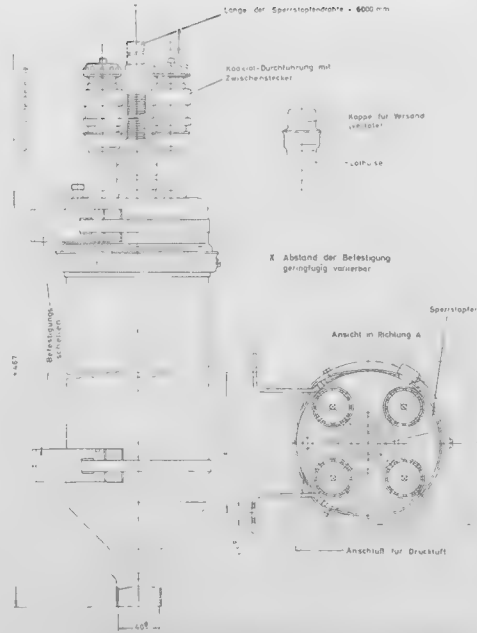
Druckdichte Aufteilungsmuffe mit Steckanschlüssen für max. 4 Koaxialpaare.
